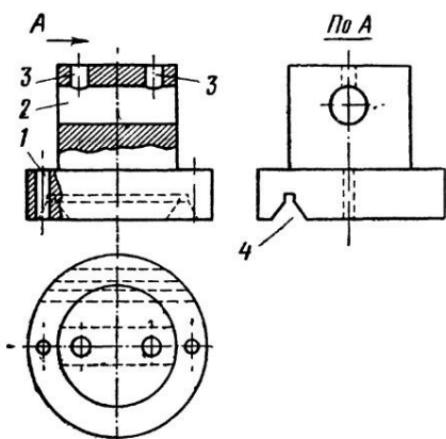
Корпус задней бабки фрезерного станка. Схема отверстий: 1 — для болта крепления к столу; 2 — для пиноли; 3 — для болта крепления пиноли; 4 — паз для направляющей станины токарного станка.
